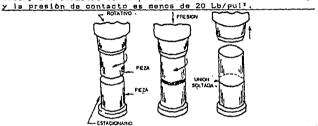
Soldadura por friccion. (Ref. 2).
